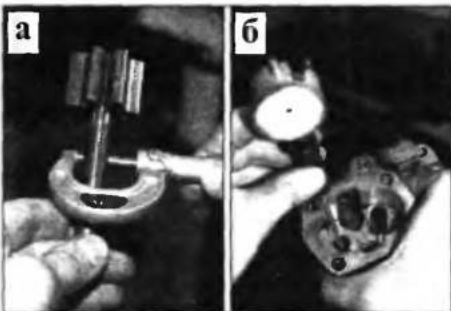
Проверка зазора в соединении ведущего валика насоса и корпуса измерением: а — диаметра валика микрометром; б — диаметра отверстия в корпусе нутромером
